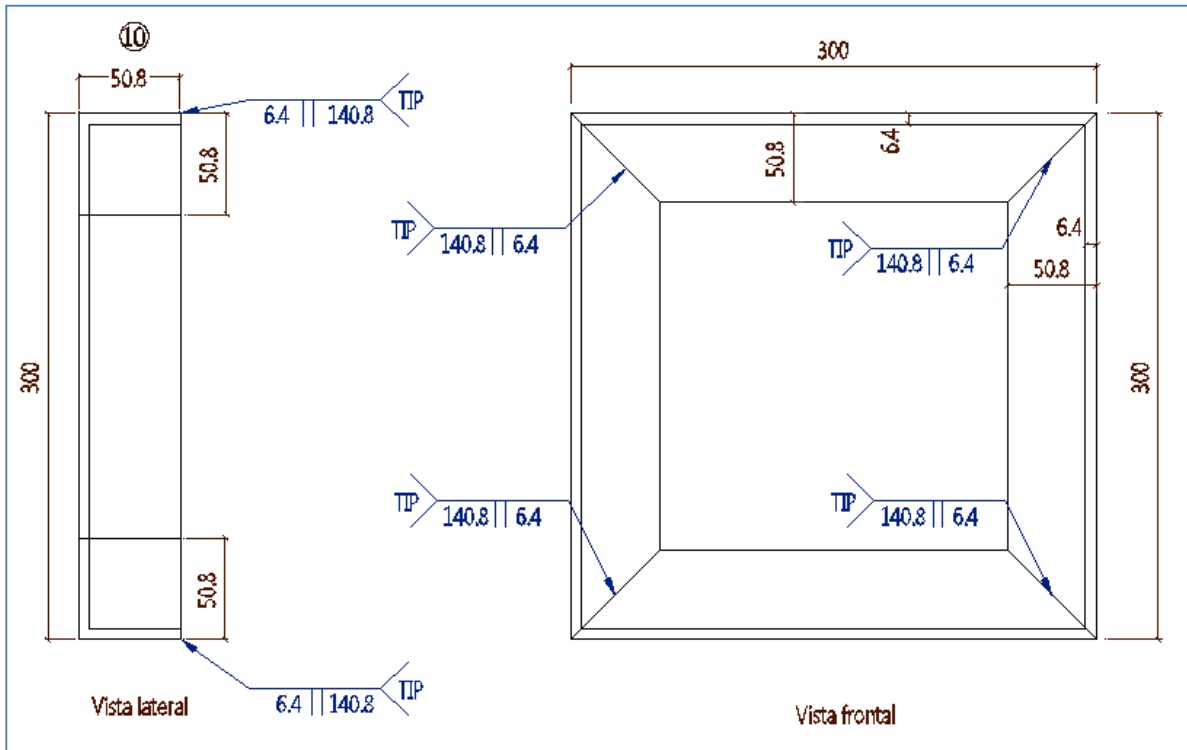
Detalle despiece pieza No.10 modelo 4 tensión.
